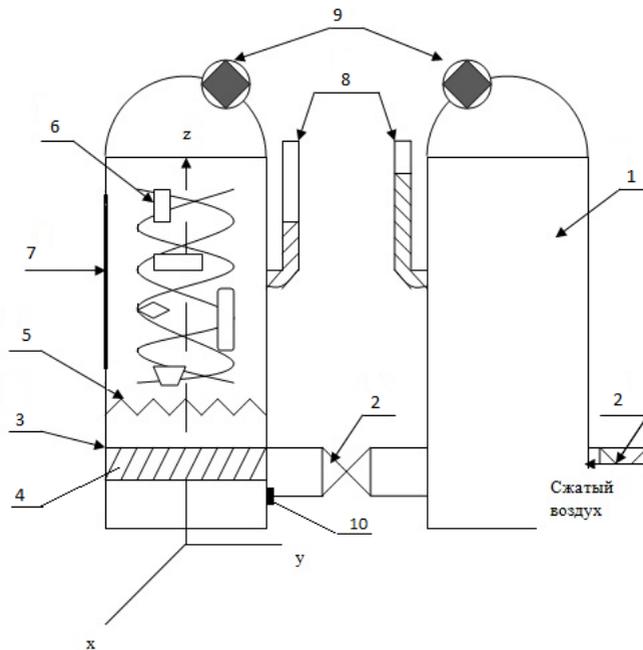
Устройство для обработки деталей в газообразных потоках:
